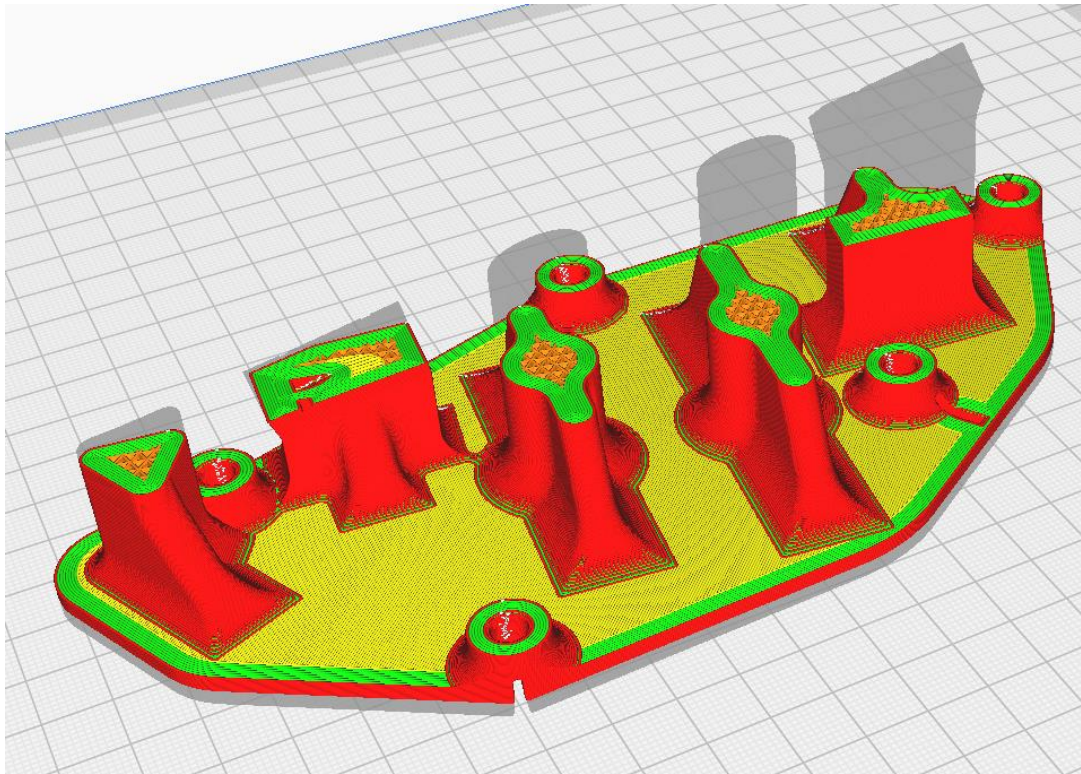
Vista módulo 1 del utillaje para pieza 2 en el laminador de Ultimaker Cura
